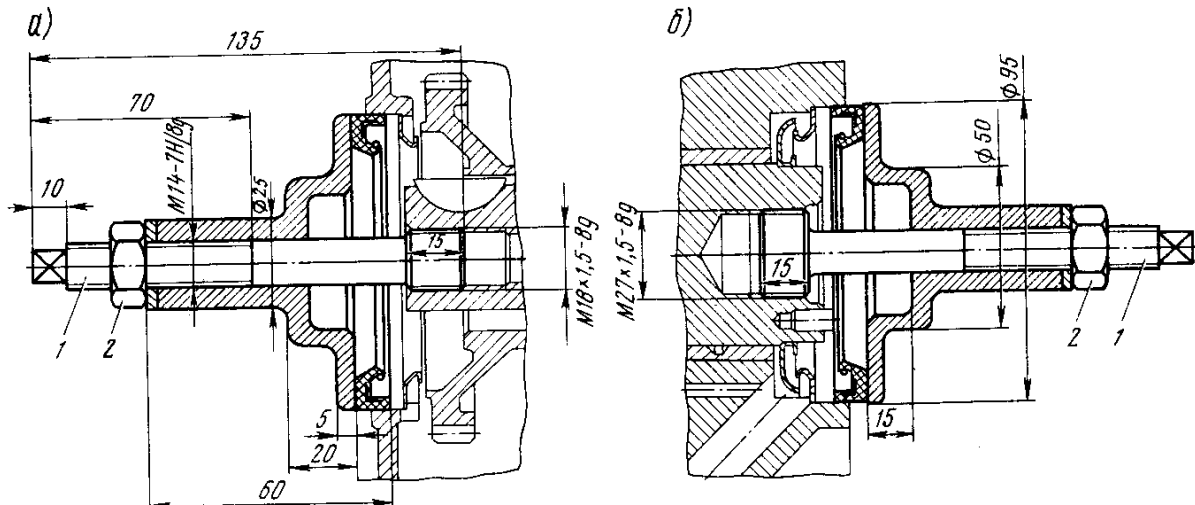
Оправка для установки манжет коленчатого вала: а — у корпуса центробежного маслоочистителя; б — со стороны маховика; 1 — винт, 2 — гайка
